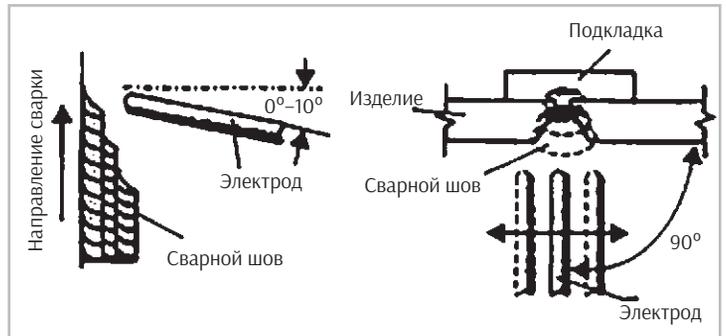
Положение электрода при сварке стыкового соединения со скосом кромок на подкладке в вертикальном положении
